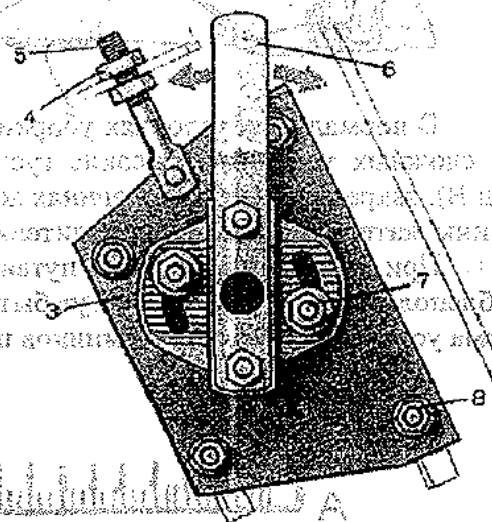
Схема механизма регулировки проставки: 3-плита; 4, 8- гайки; 5-винт; 6-рукоятка; 7-болт
